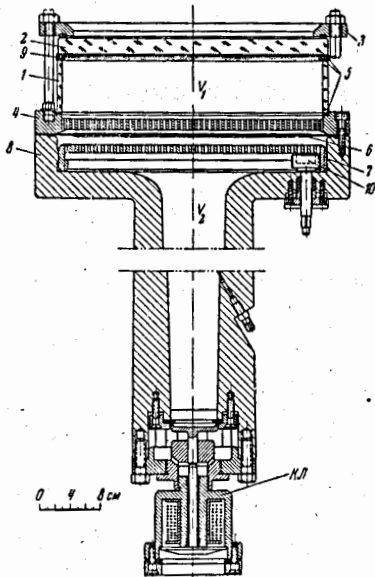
Камера Вильсона. 1 — стеклянный цилиндр; 2 — стеклянный диск; 3 — прижимной фланец; 4 — неподвижная решетка; 5 — резиновые уплотнения; 6 — мембрана; 7 — подвижная решетка; 8 — корпус камеры; 9 — латунное кольцо с натянутыми на нем проволочками; 10 — пестерли
